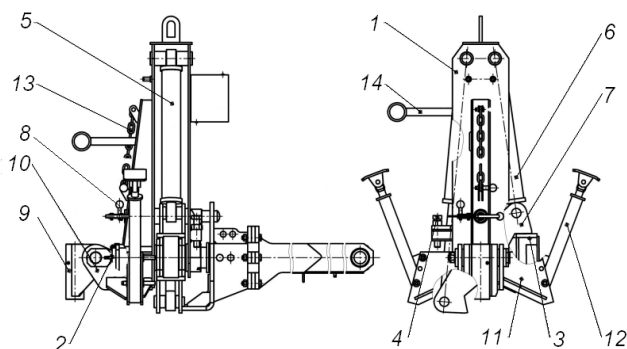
Механизм оборота рамы: 1 – корпус; 2 – шлицевой вал с фланцем; 3 – упор; 4 – регулировочный болт; 5, 6 – гидроцилиндры; 7 – рычаг; 8 – фиксатор; 9 – крестовина; 10 – понизитель корпуса; 11, 14 – кронштейны; 12 – опора; 13 – цепь
